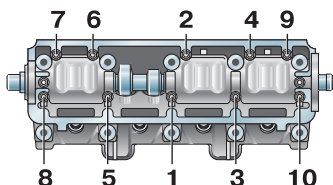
Порядок затягивания гаек крепления корпусов подшипников распределительного вала.
